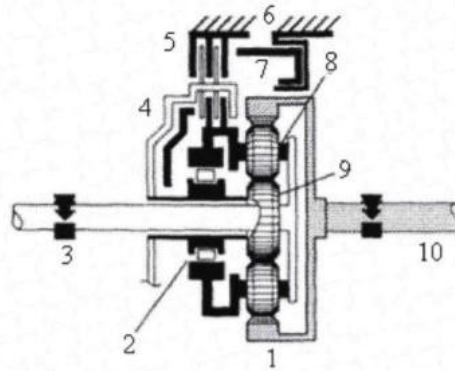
Підвищувальний планетарний ряд: 1 - ВЦК; 2 - муфта вільного ходу; 3 - вал турбінного колеса; 4 – блокувальна муфта; 5 - гальмо МЦК; 6 - картер; 7 - поршень; 8 - водило; 9 - МЦК; 10 - вхідний вал основної коробки передач.
